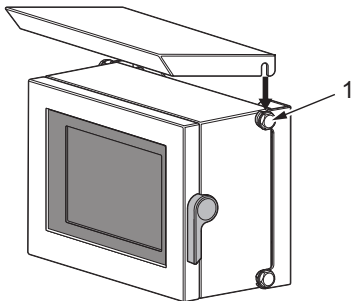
Befestigung des MI an der Wandhalterung
